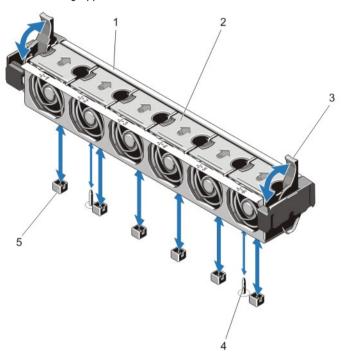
Lüfterbaugruppe entfernen und installieren
